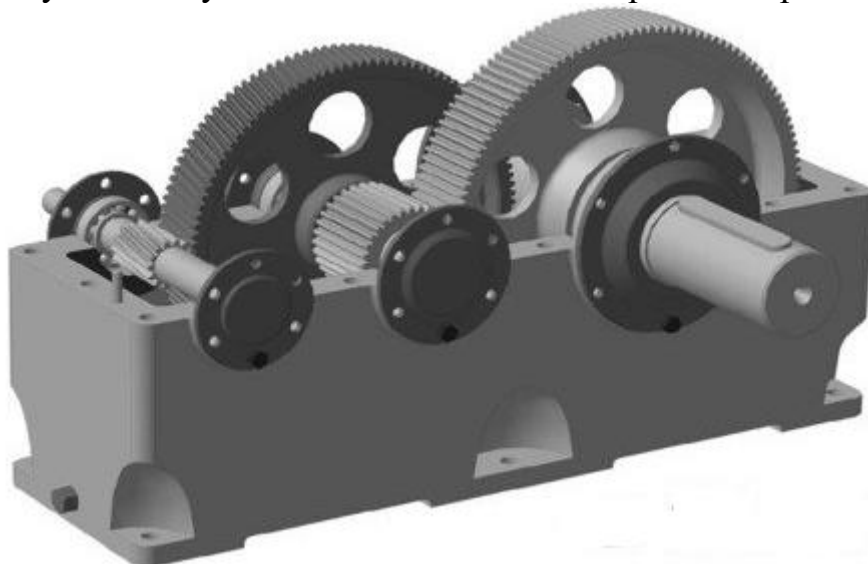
Редуктор двоступінчастий циліндричний косозубий
